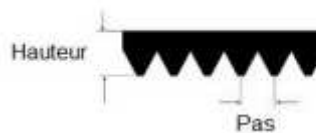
différentes section d'un courroie striée (Source : ISO 1813)
